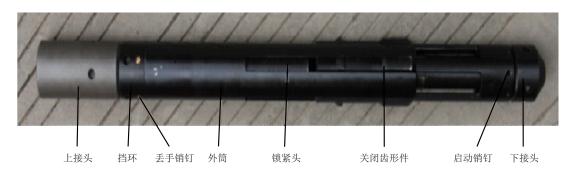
滑套关闭工具实物图 Fig. 9 Closure tool of sliding sleeve
